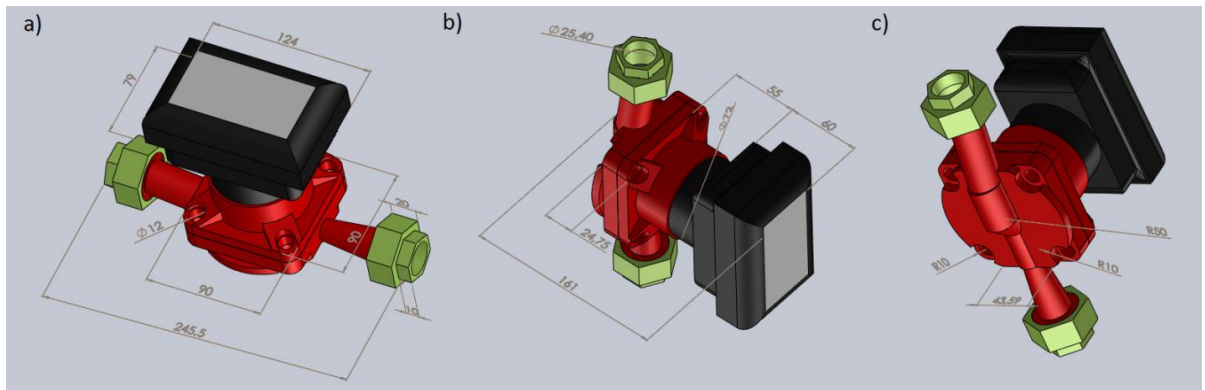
Desenho tridimensional da bomba ECO QUANTUM 1035 e as características geométricas na: a) 1ª vista, b) 2ª vista e c) 3ª vista.
